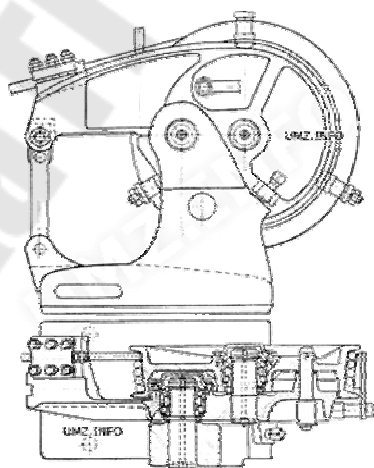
Механизм крепления неподвижной ветви талевого каната
